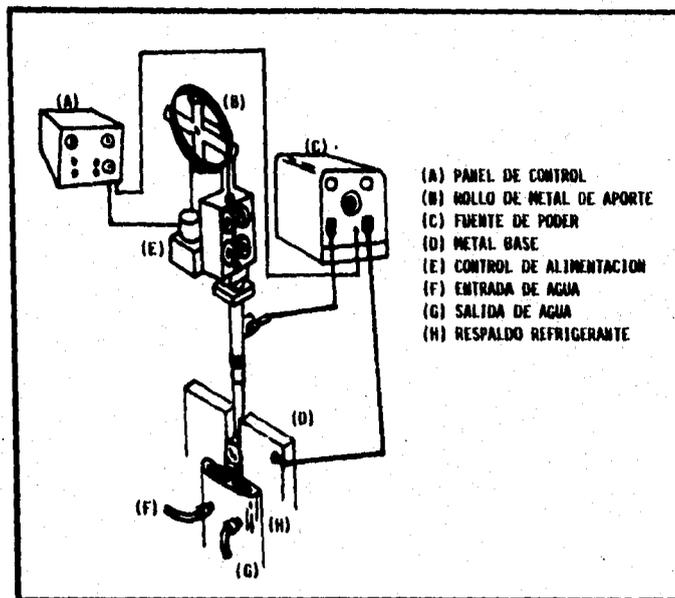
DETALLE DEL PROCESO DE SOLDADURA ESM.
